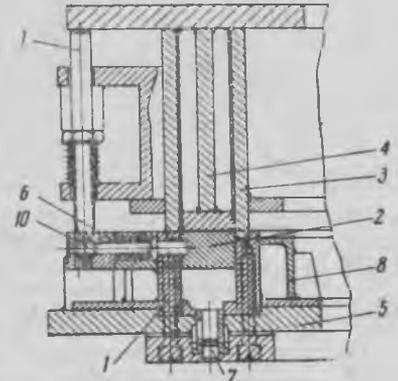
Схема пресс-формы со съемной загрузочной камерой и толкателем
